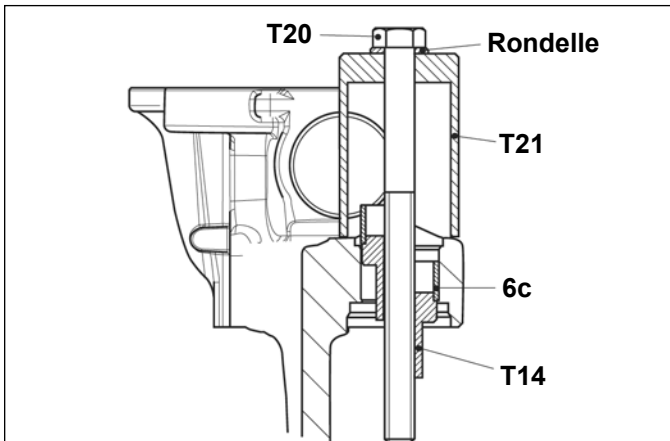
VUE EN SECTION : DÉPOSE DE LA DOUILLE DE LA COURTE TIGE DE GUIDAGE
